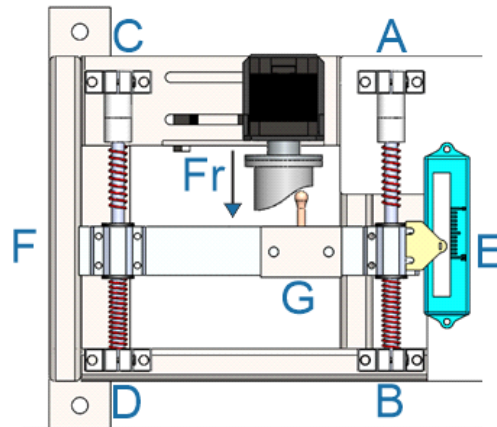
Vista planta mecanismo leva cilíndrica.
